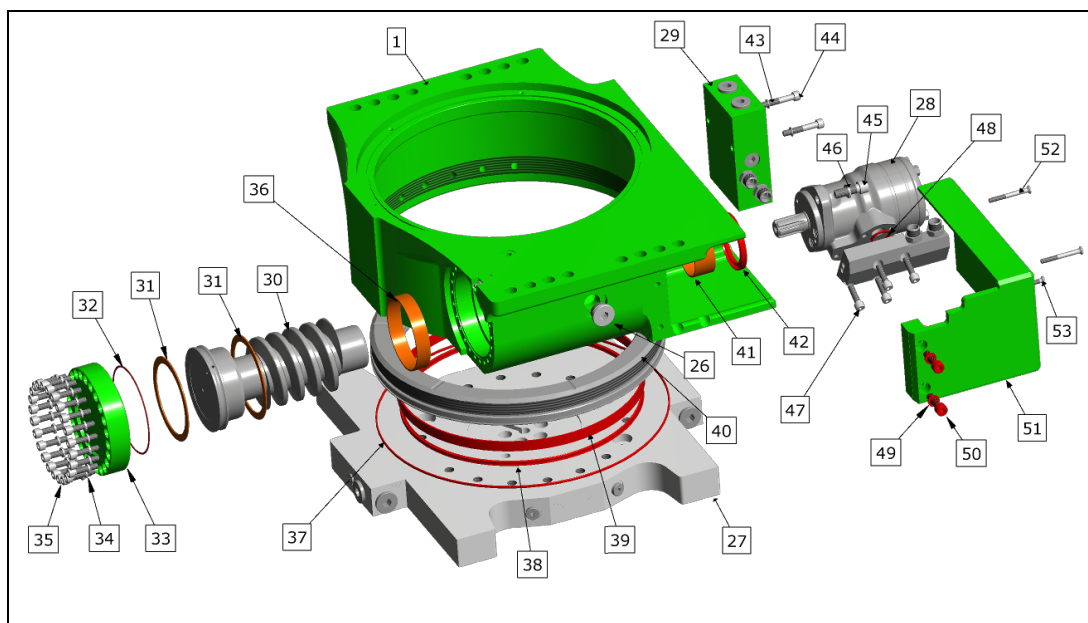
exemple pièces de rechange RotoBox 2
